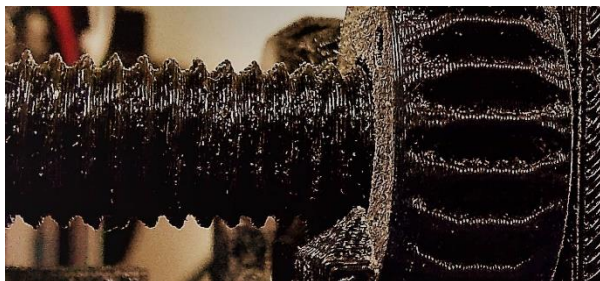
Pieza que presenta una cuerda de buena calidad y útil para un mecanismo.
